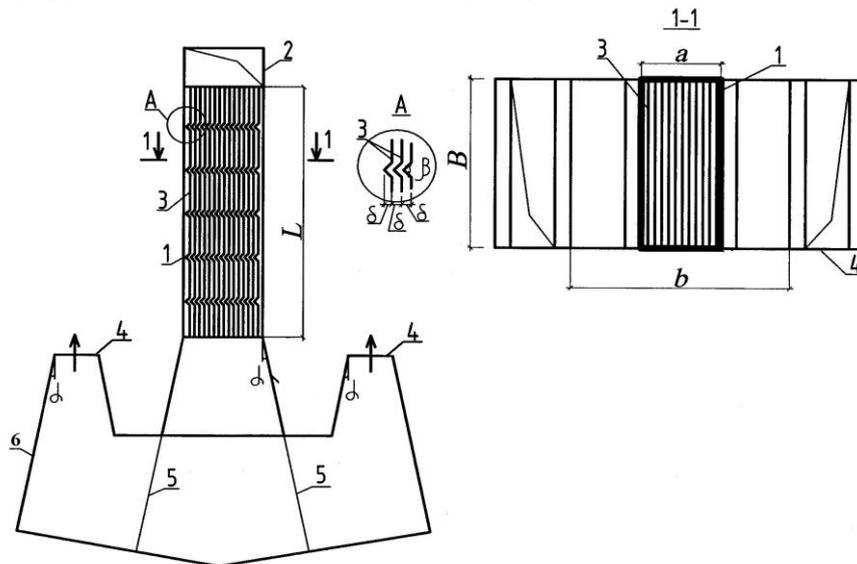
Сепаратор туманов с изогнутыми пластинчатыми адгезионно-осадительными элементами: 1-корпус сепаратора; 2-воздуховод равномерной раздачи; 3- изогнутые пластины; 4-стабилизирующие конфузорные патрубки; 5-сетки-укрупнители капель; 6- бункер
